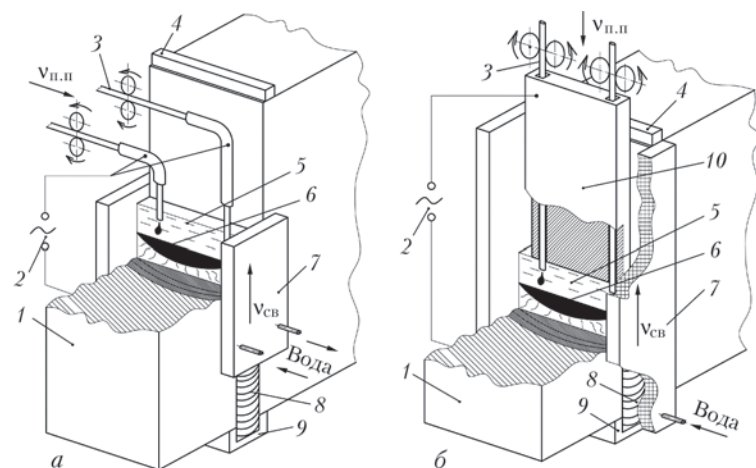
Схемы ЭШС проволочными электродами (а) и плавящимся мундштуком (б): 1 — свариваемые изделия; 2 — источник питания; 3 — сварочная проволока; 4 — выводная планка; 5 — шлаковая ванна; 6 — металлическая ванна; 7 — водоохлаждаемая формирующая планка (ползун); 8 — сварной шов; 9 — входной карман; 10 — мундштук
